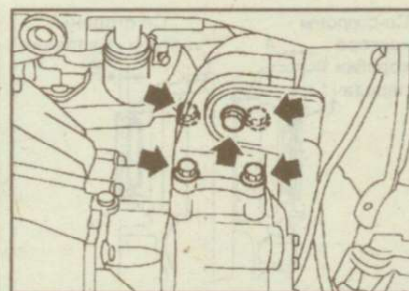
Расположение болтов крепления левой опоры силового агрегата
